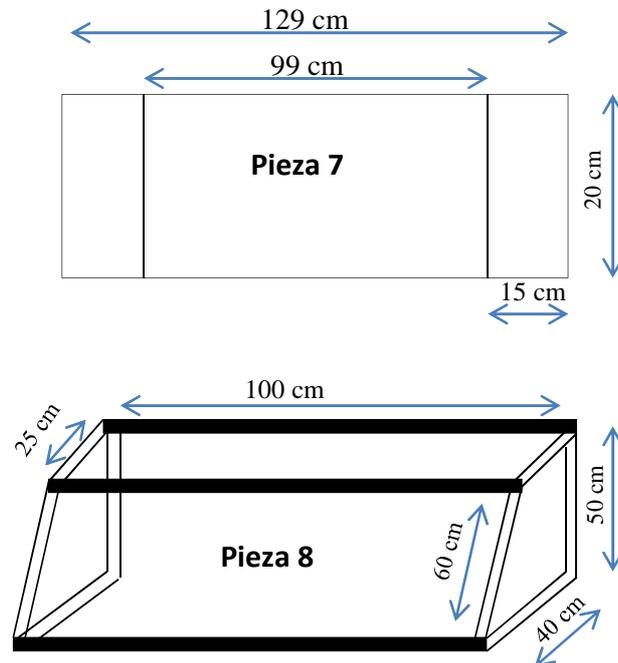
Estructura con cubierta de vidrio y Fondo de Bandejas del Autoservicio
